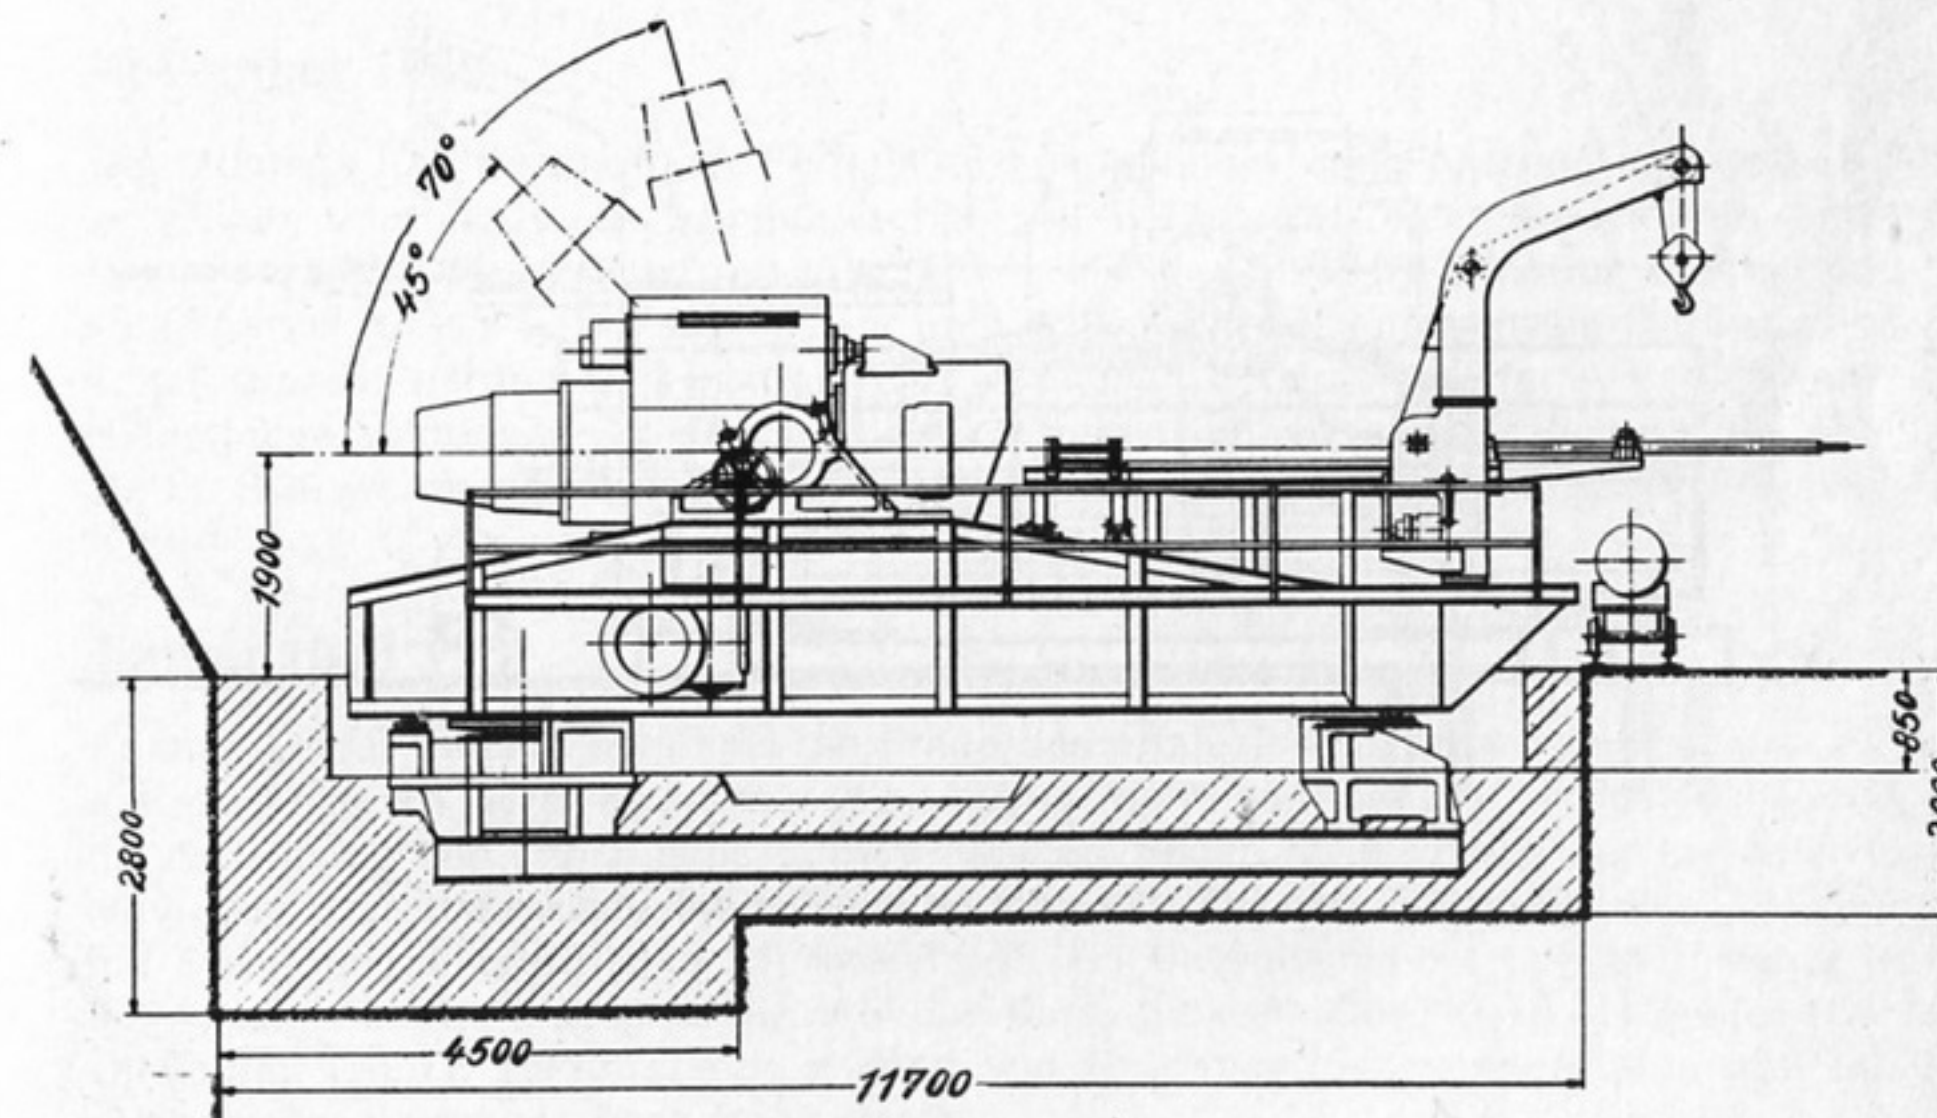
Ortsfester Einbau der A-Lafette auf Betonfundament
